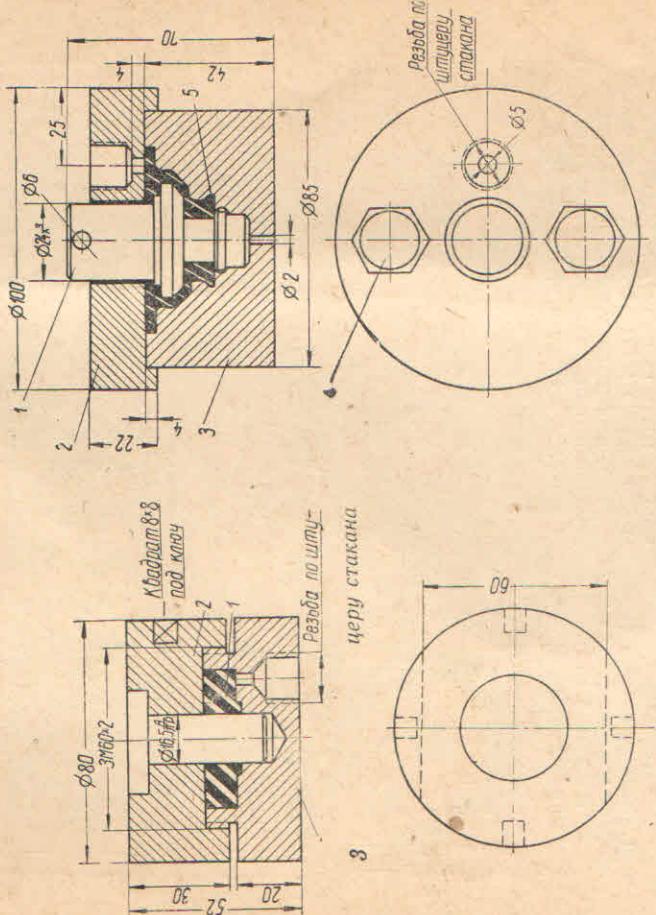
Пресс-форма в сборе с деталью № 20—1302045 — подушка радиатора в сборе:
